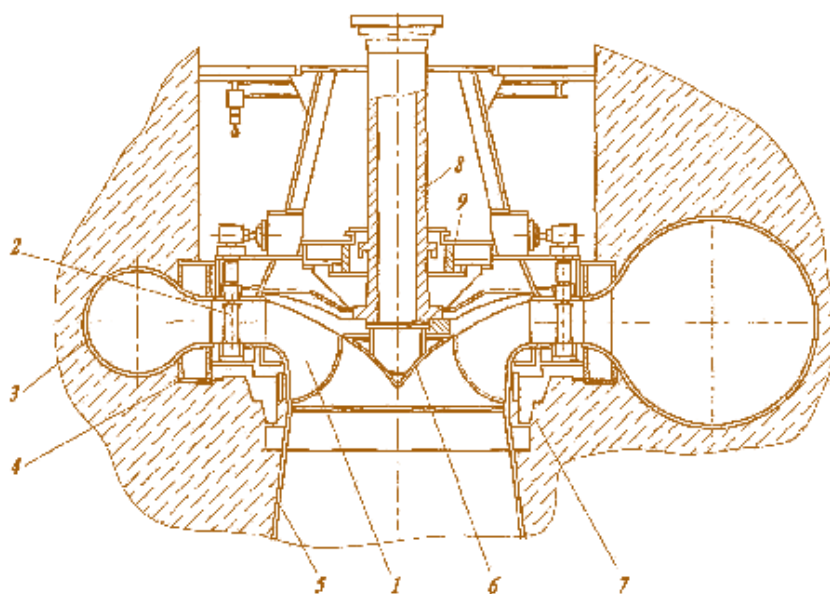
Розріз по насос-турбіні Загорської ГАЕС: 1 – робоче колесо; 2 – лопатки напрямного апарата; 3 – спіральна камера; 4 – статор; 5 – відсмоктувальна труба; 6 – конус робочого колеса; 7 – колектор; 8 – вал; 9 – напрямний підшипник
